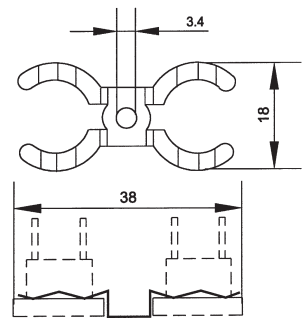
Zwillingsflansch spez. für 2 Thermostate
